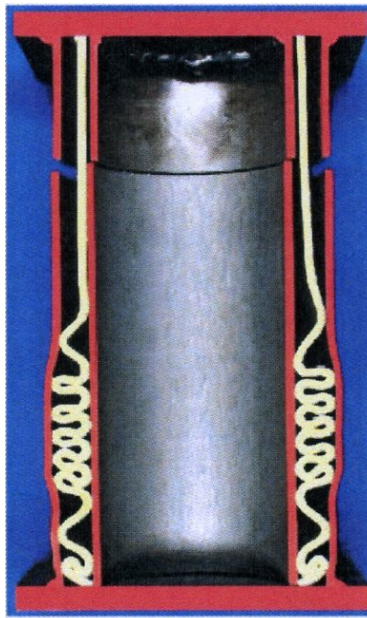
Vista sección sostenida con bandas de corte.
